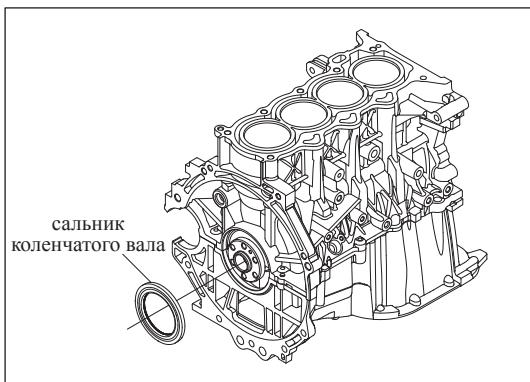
Установка заднего сальника коленчатого вала
